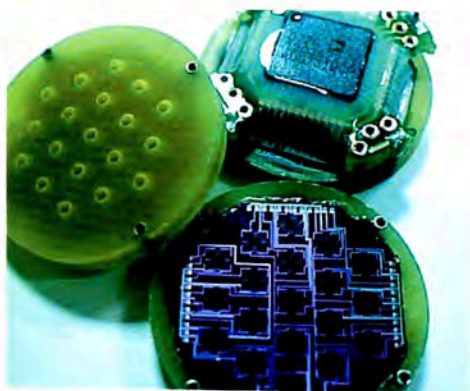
Тактильный датчик МИПД-19 и корпус для испытания под давлением
